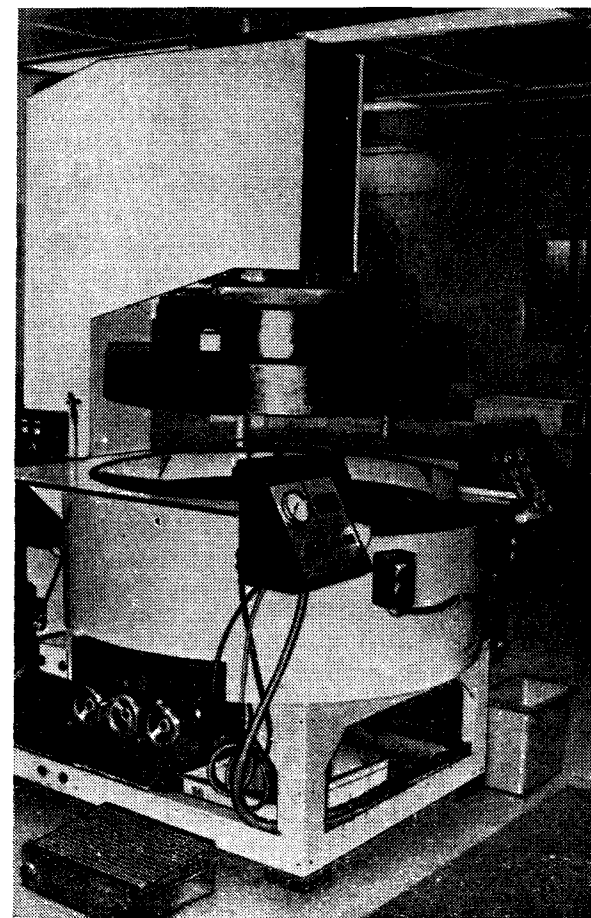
Станок для двусторонней шлифовки подложек.
